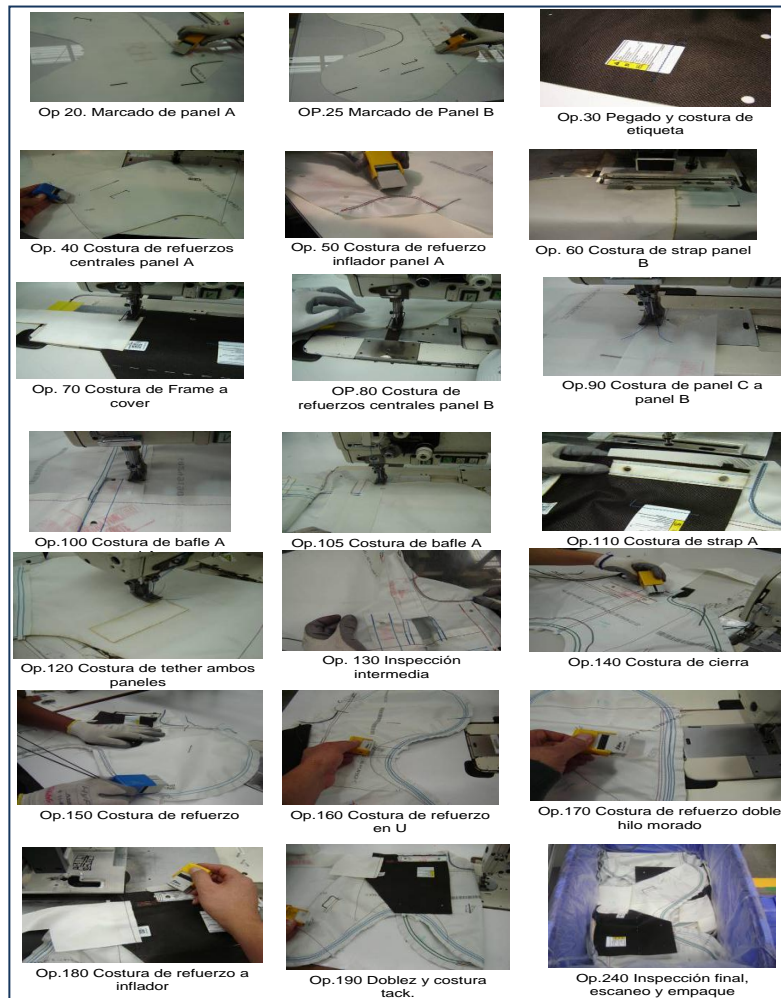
7 Descripción del proceso de manufactura de bolsa de aire
